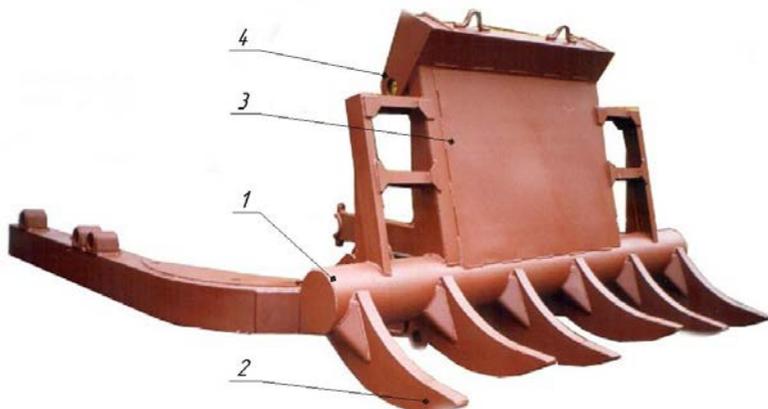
Орган корчевальный в сборе с рамой универсальной:
